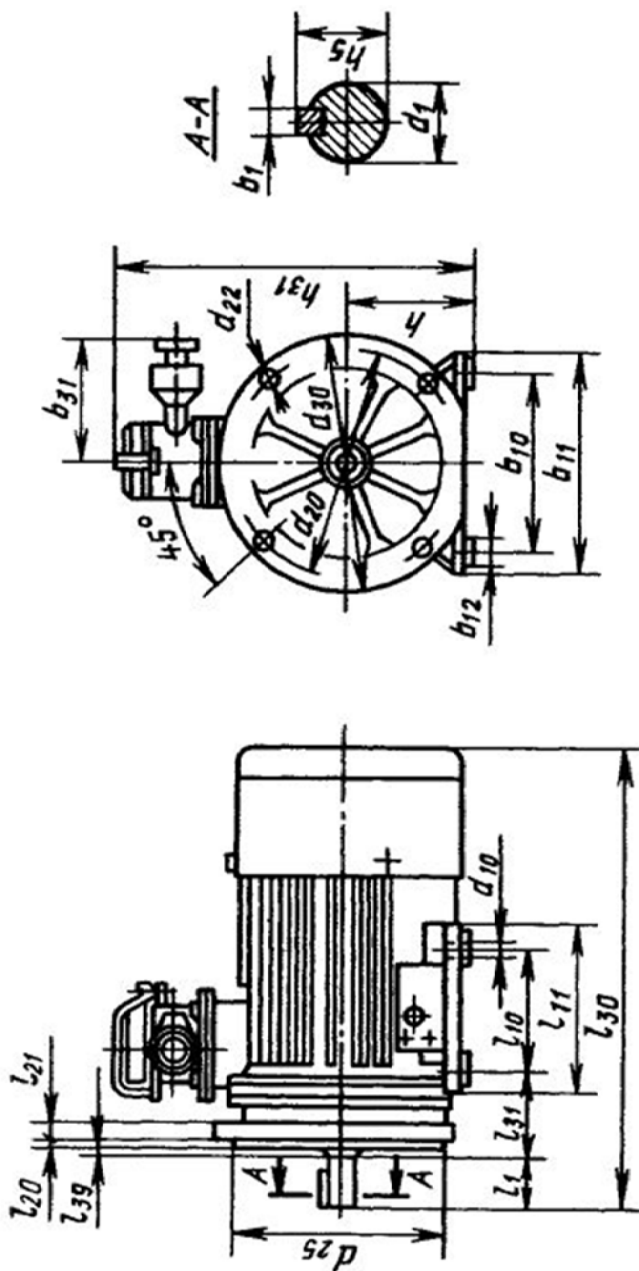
Габаритный чертеж электродвигателя серии ВАО на лапах + фланец
